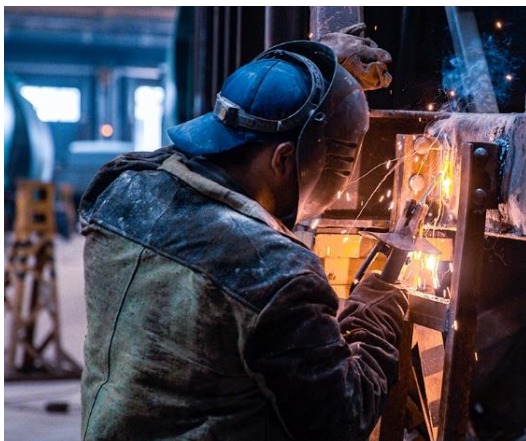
Выполнение операции ремонтной сварки стенки вагона
